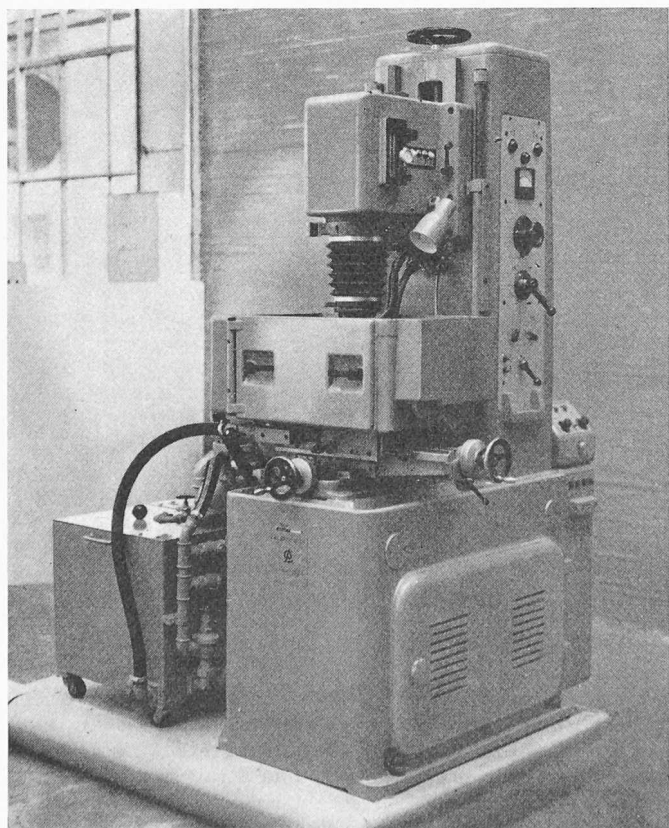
Funkenerosionsmaschine. Maximaler Materialabtrag beim Schruppen 423 mm³/min, Oberflächengüte beim Schlichten 0,3 μ in mittl. Quadratwert gemessen, Bearbeitungsgenauigkeit ± 0,005 mm
